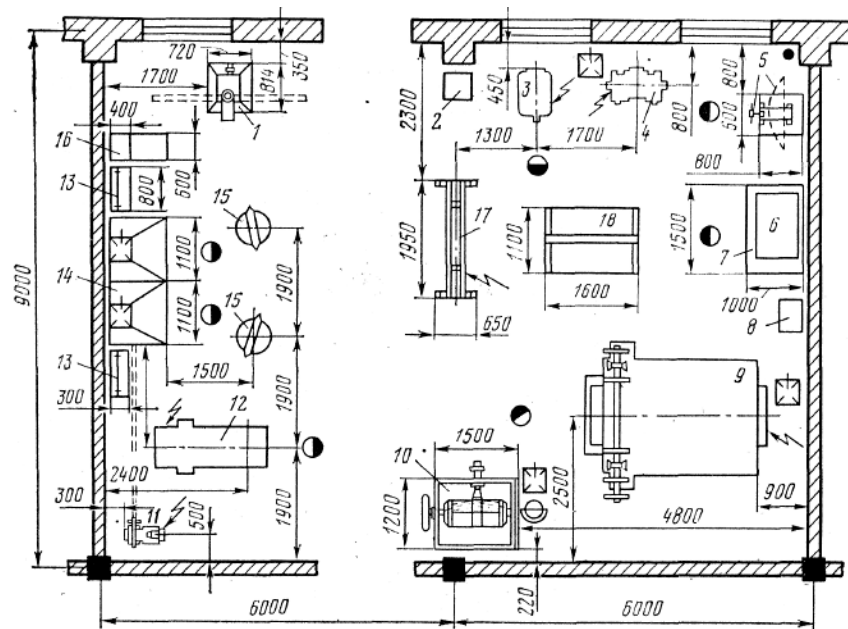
Ковальське відділення ПАТ: 1 - стэнд для рихтування ресор; 2 - ящик для піску; 3 - вертикально-свердлувальний верстат; 4 - обдирно-шліфувальний верстат; 5 - стэнд для зборки ресор; 6,7 - правильна плита на підставці; 8 - щит для управління піччю; 9 - камерна електрична піч; 10 - установка для загартування ресорних листів; 11 - повітродувка до горна; 12 - пневматичний молот; 13 - скриня для кузнечного інструменту; 14 - ковальський горн на два вогні; 15 - ковадло; 16 - ящик для вугілля; 17 - стэнд для випробування ресор; 18 - стелаж для ресорних листів
